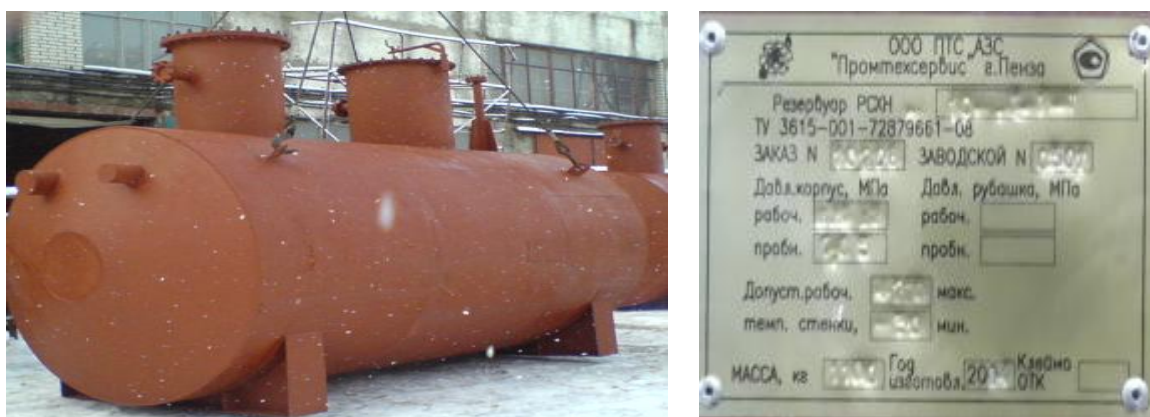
Внешний вид резервуара и маркировочной таблички
